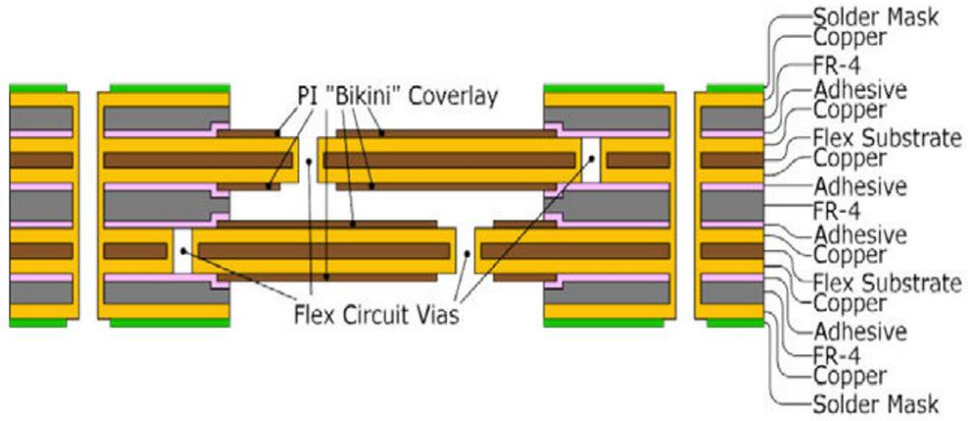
Örnek rigid-flex-rigid PCB kartı
